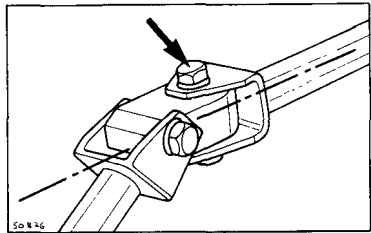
Перед затяжкой болта выровняйте ось промежуточного вала с центром соединительного блока
